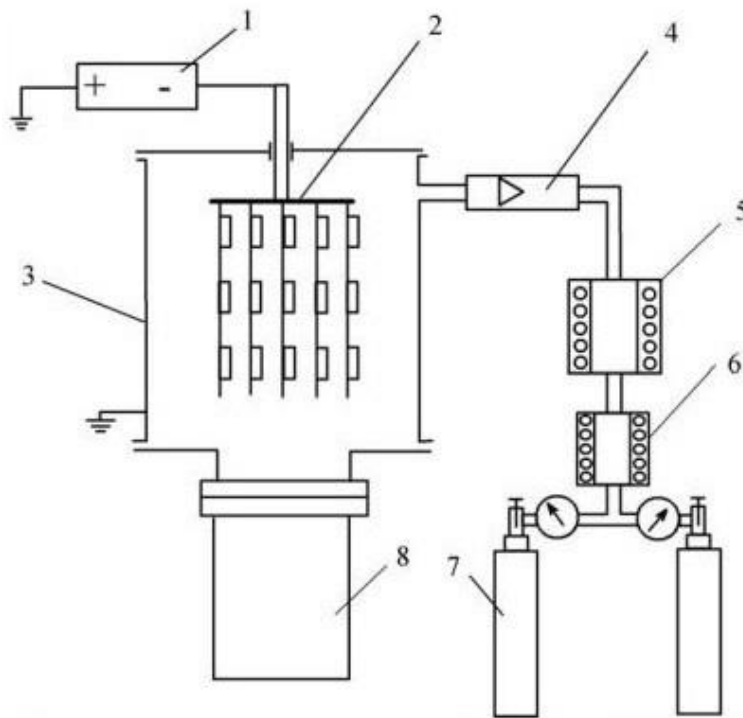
Схема муфельної печі для азотування: 1 - джерело живлення; 2 - заготовка з виробами; 3 - вакуумна камера; 4 - ротаметр; 5,6 - фільтри; 7 - балони з газом; 8 - форвакуумний насос.
